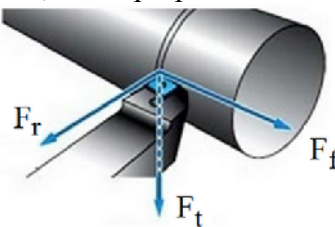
Las tres componentes de la fuerza de corte [89].
